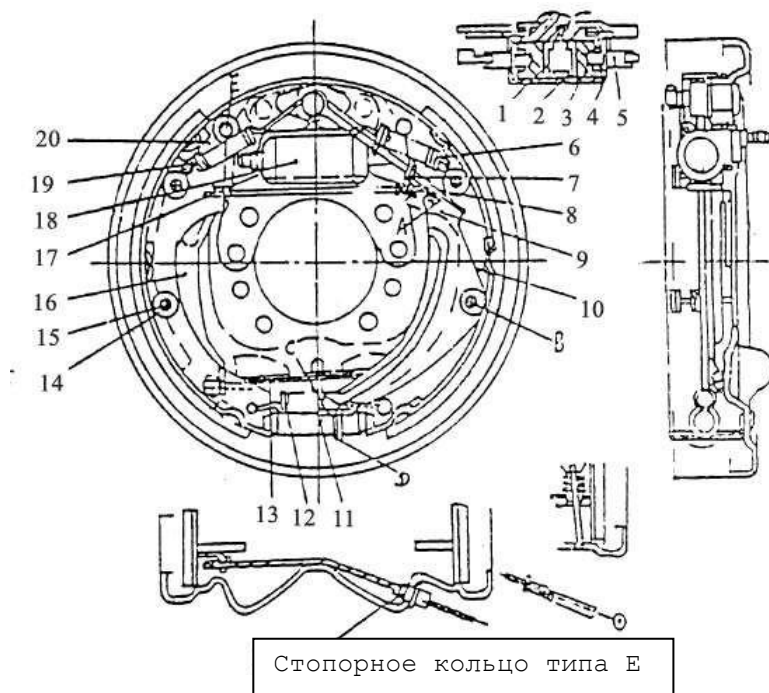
Колесный тормоз для погрузчиков 2 и 2,5 т:
